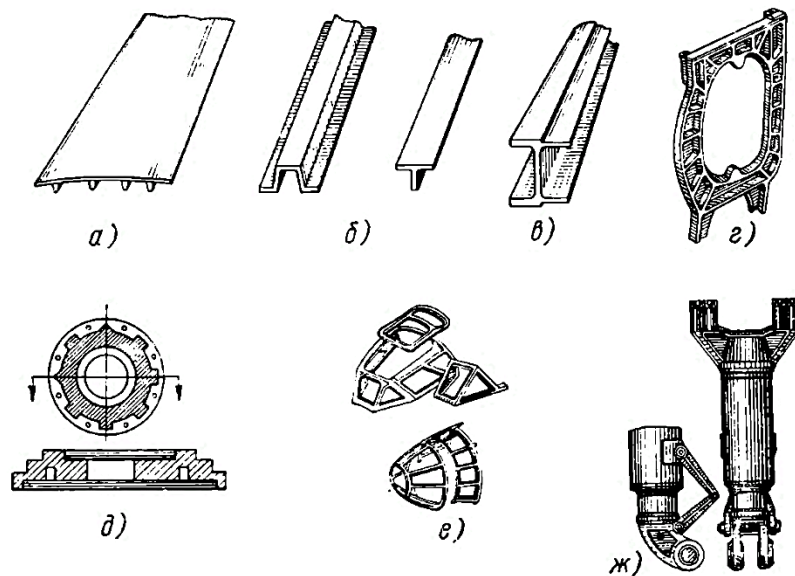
Типові деталі, що виготовляються обробкою різанням:
